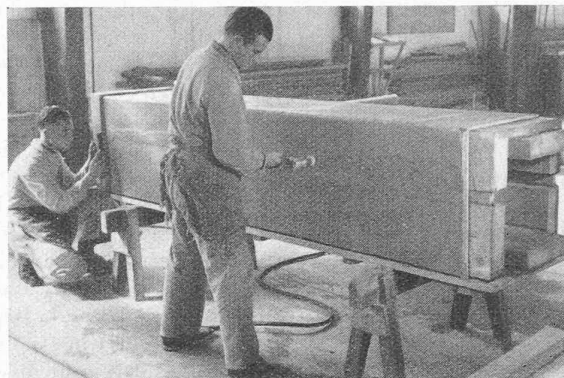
Soudure exécutée avec un marteau pneumatique.
